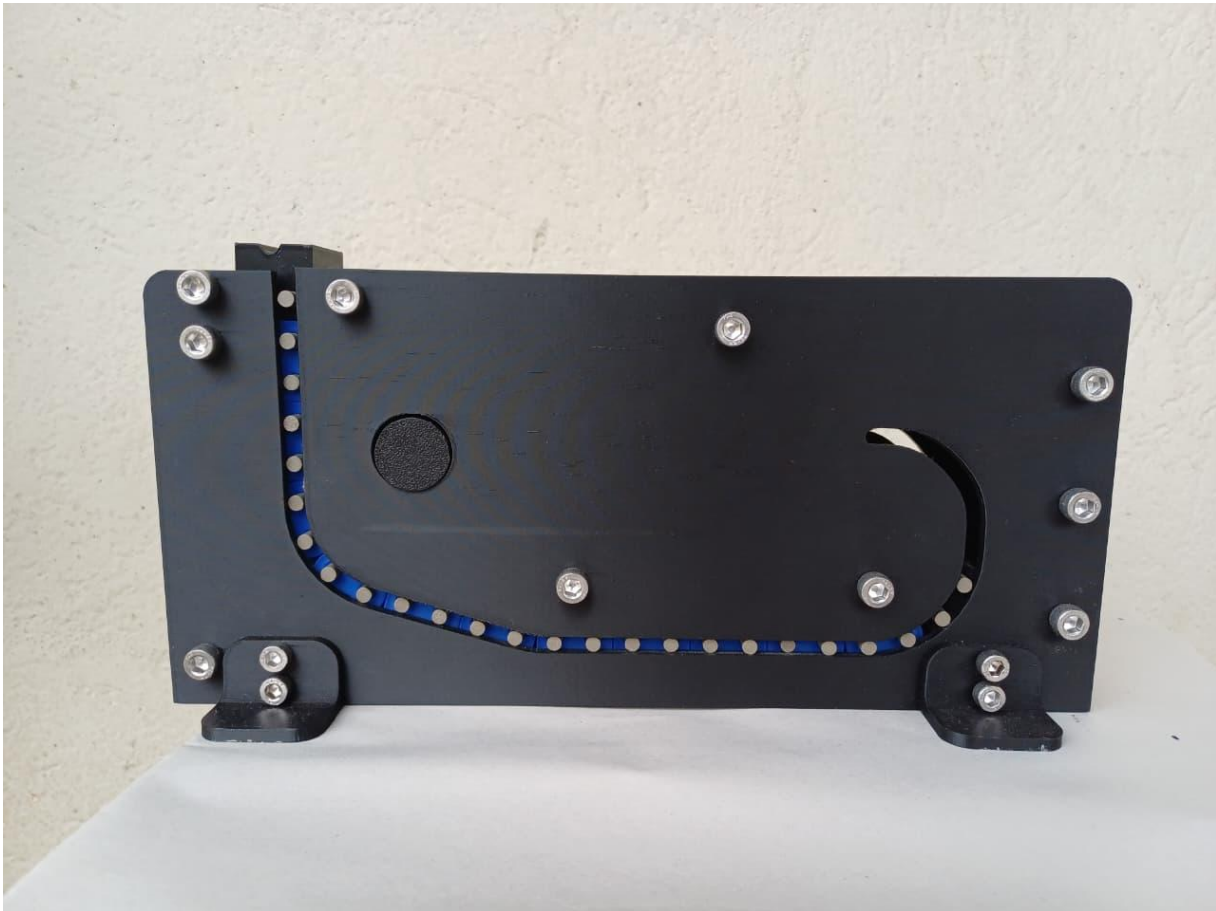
Vista de la cadena retraída sobre el carril.
